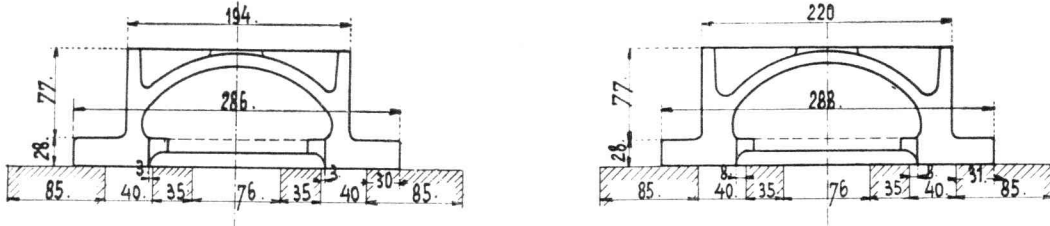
Dampfschieber und Steuerkanten für Hoch- und Niederdruckzylinder, Serie 108.
